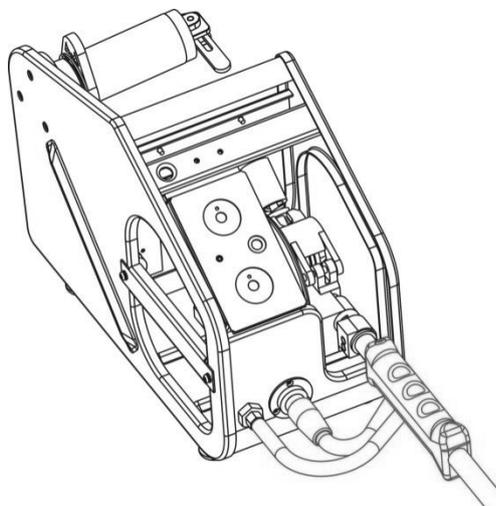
Принципиальная схема подключения сварочной горелки к механизму подачи проволоки
